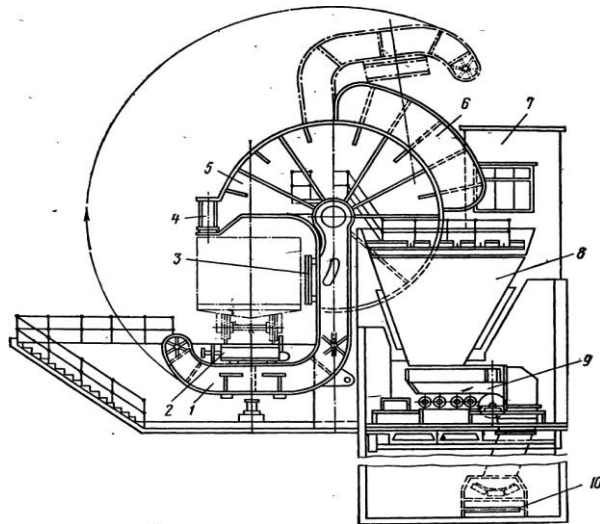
Стационарный боковой вагоноопрокидыватель.
